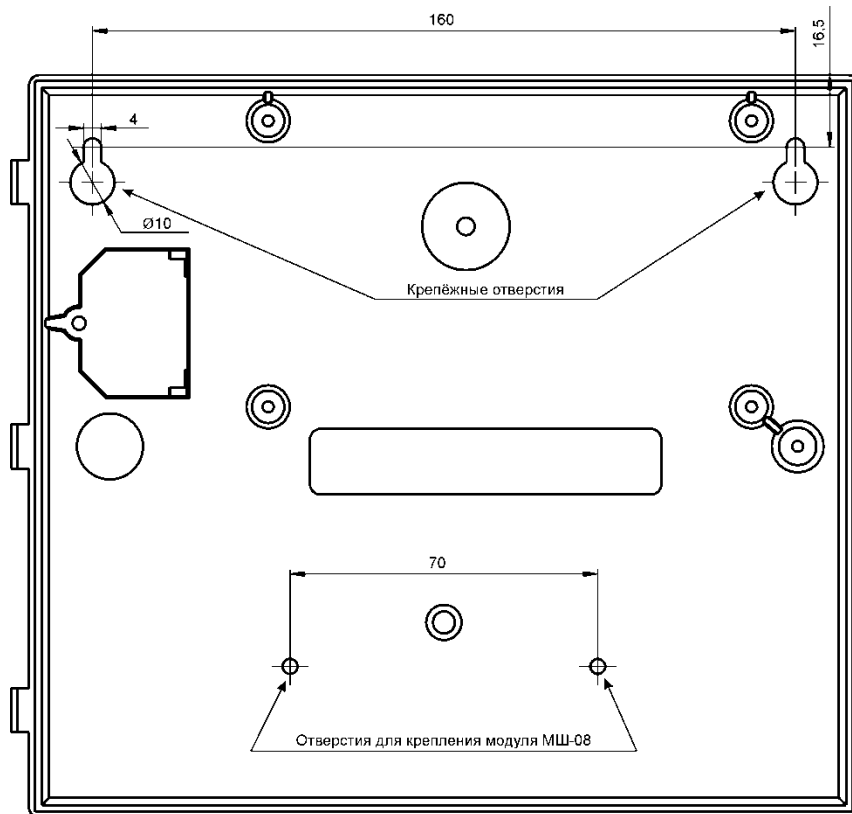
Установочный чертёж корпуса (вид изнутри)
